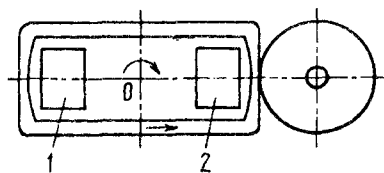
Схема фрезерования заготовки на двухпозиционном поворотном столе
